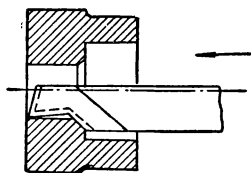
Комбинированный резец для растачивания и снятия фаски.
